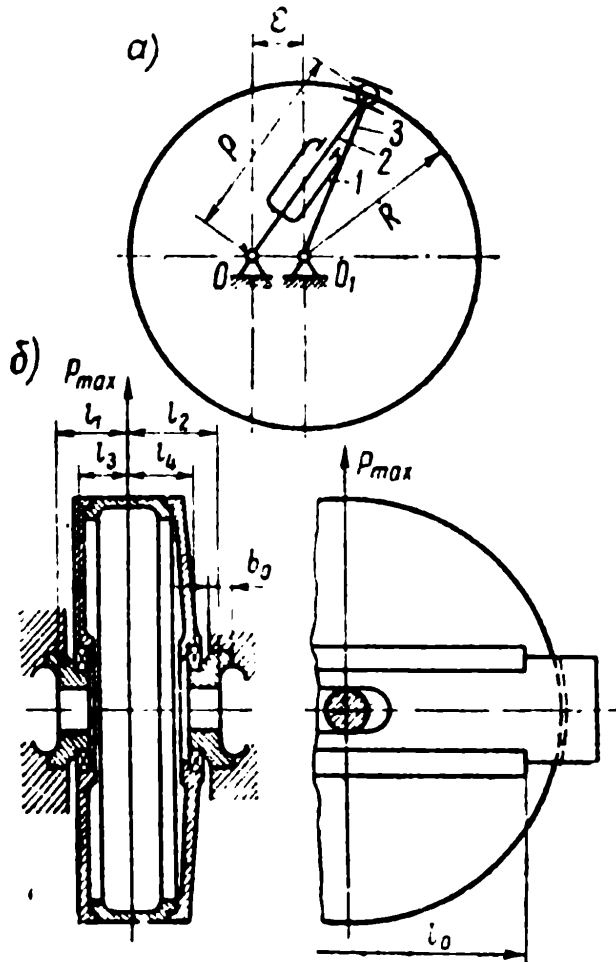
Установка цилиндрической направляющей в корпусе: а — кинематическая схема; б — цилиндрическая направляющая
